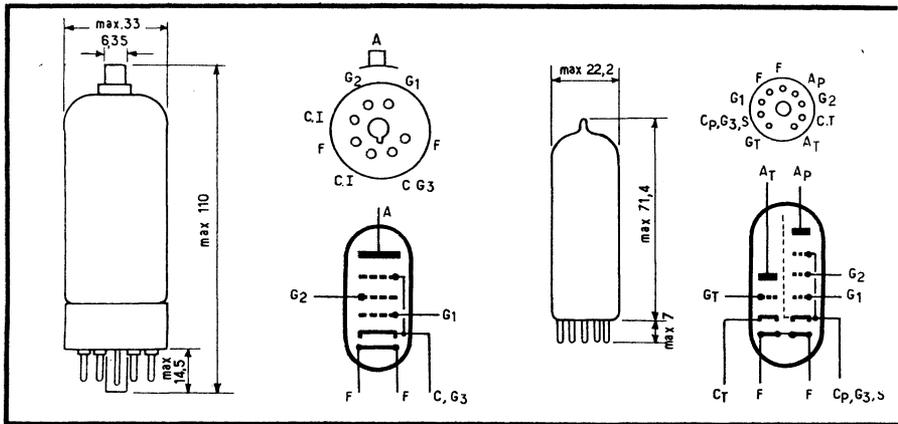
Dimensions de l'ampoule et brochage des tubes PL 36 et PCL 82.
